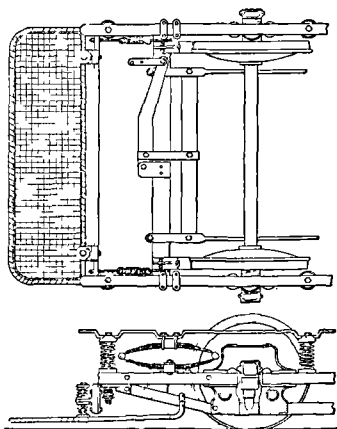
Garde-roues Peckham. Plan et élévation.
